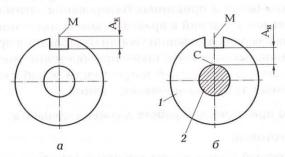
Схема обработки паза: a — чертеж конструктора;  $\delta$  — выбор исходной базы (ИБ = УБ)
